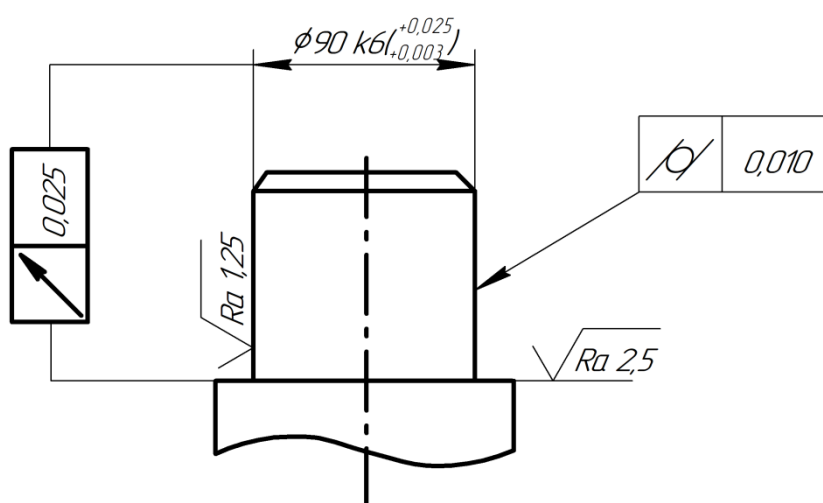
Обозначение допусков размера вала
